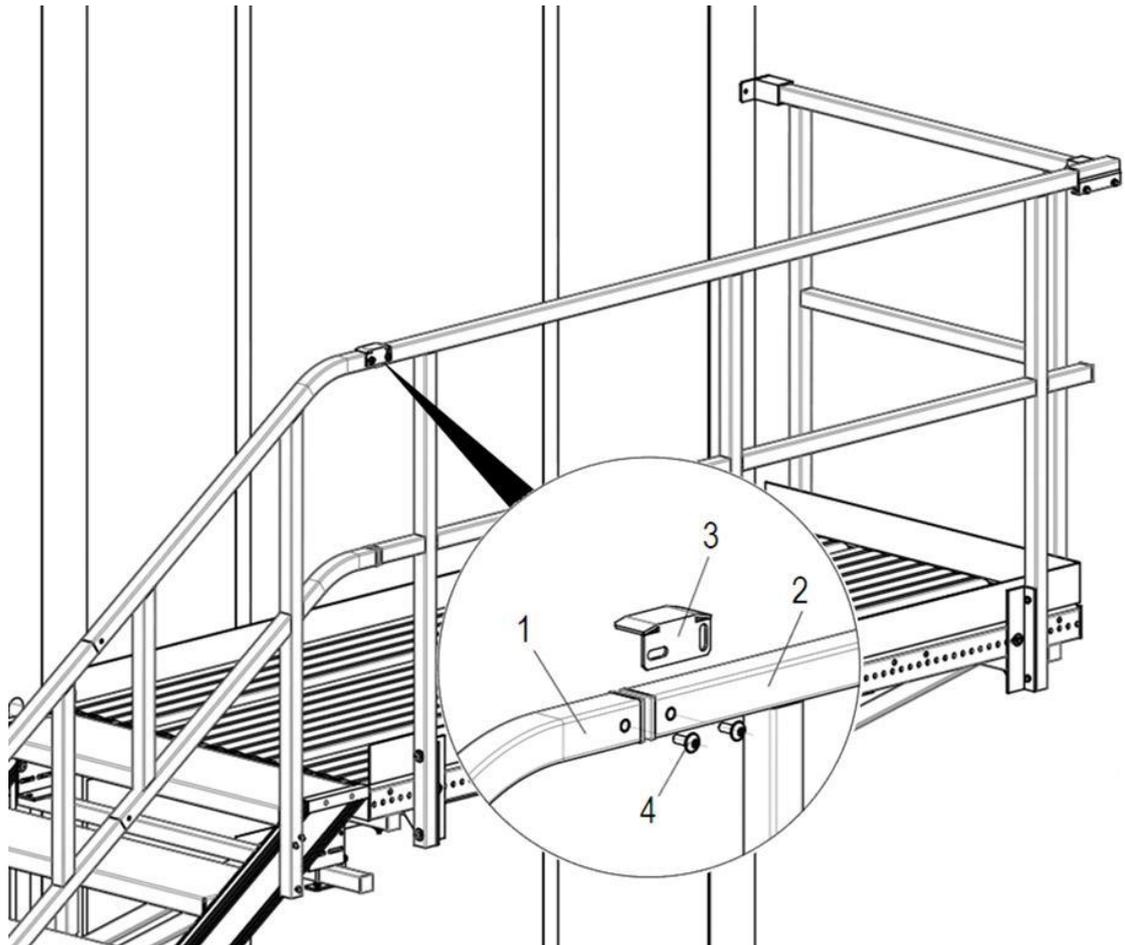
Verbinder für Laufsteg- und Treppengeländer anschrauben
